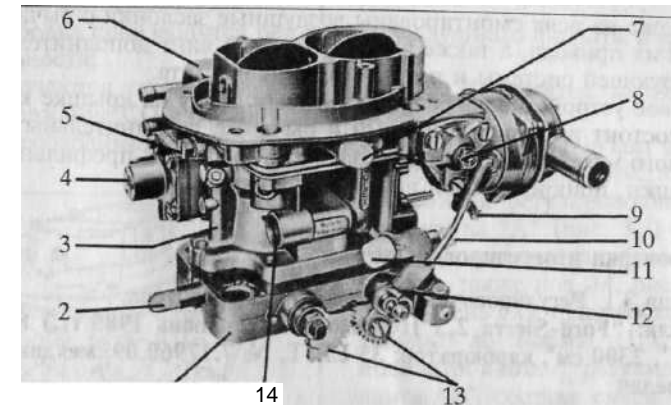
Д. Двухкамерный карбюратор "Solex" 38/38 ЕЕИТ (вид со стороны зубчатых секторов):
